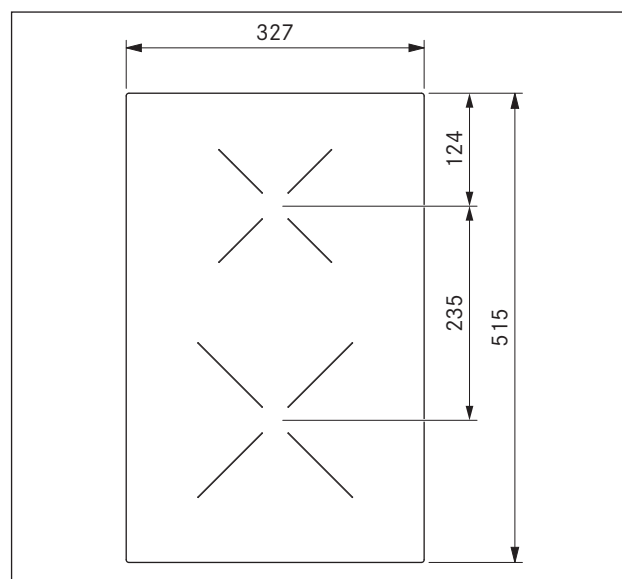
Dimensões do aparelho CKI, vista de cima
